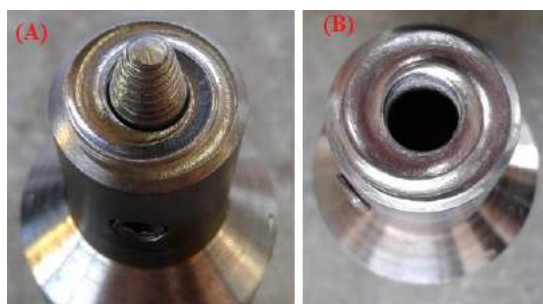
Ferramenta de soldagem, (a) antes de polir e com o pino, (b) depois de polir sem o pino
